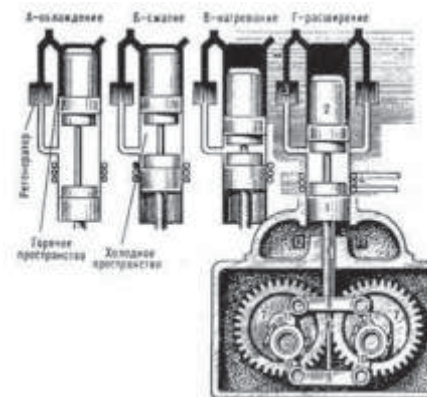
Устройство двигателя Стирлинга: 1 – рабочий поршень; 2 – поршень-вытеснитель; 3 – регенератор; 4 – охладитель; 5 – шток рабочего поршня; 6 – шток поршня-вытеснителя; 7 – зубчатые колеса; 8 хомут рабочего поршня; 9 – хомут поршня-вытеснителя; 10 – кривошип поршня-вытеснителя; 11 – кривошип рабочего поршня; 12 – буферная полость. А – охлаждение: поршень-вытеснитель находится в горячем пространстве, большая часть газа прокачивается в холодное пространство, рабочий поршень – в крайнем нижнем положении. Б – сжатие: рабочий поршень движется вверх, сжимая холодный газ. В – нагревание: поршень-вытеснитель движется вниз, большая часть сжатого холодного газа оказывается в горячем пространстве.
